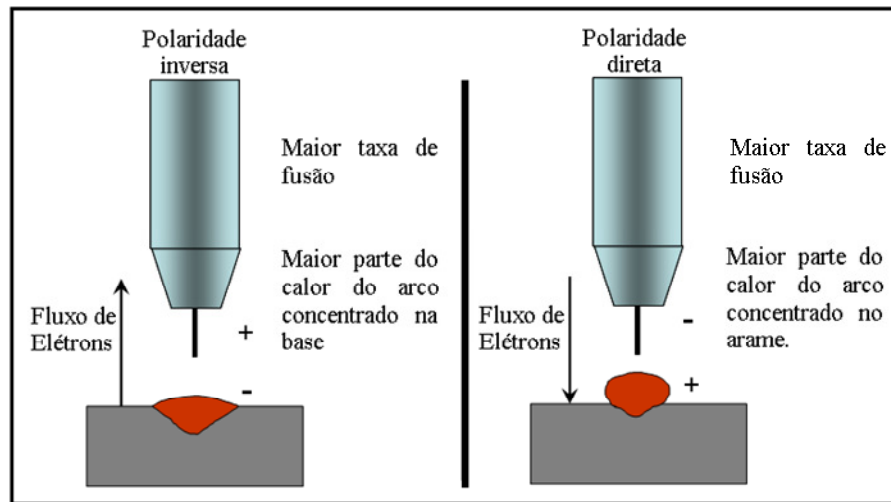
Características do cordão de solda para soldagem na CC+ e CC- (modificado TALKINGTON, 1998)
